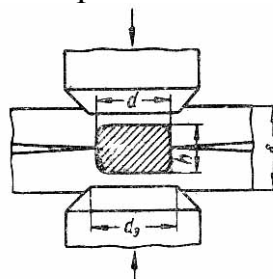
Сечение сварной точки d – диаметр ядра; h – толщина ядра; $d_э$ – диаметр контактной поверхности электрода; δ - суммарная толщина свариваемых деталей
